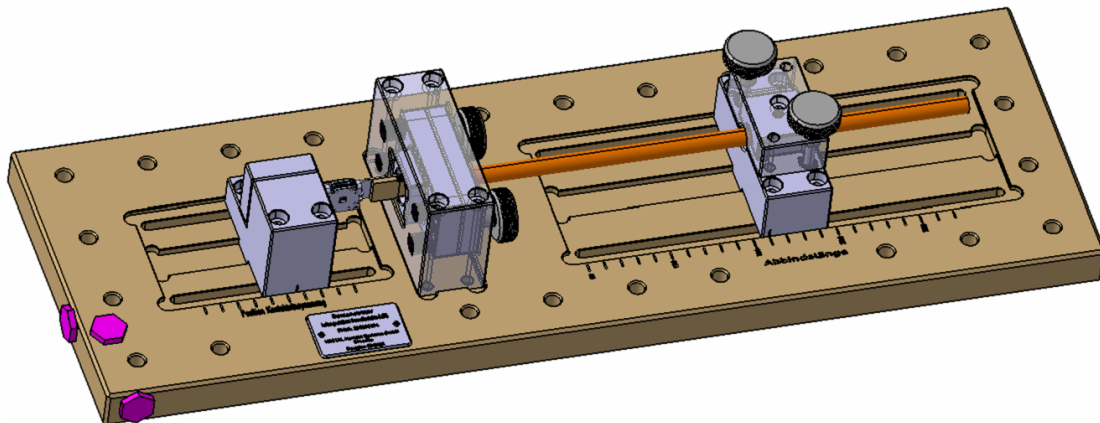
Gesamtansicht des mechanischen Aufbaus
